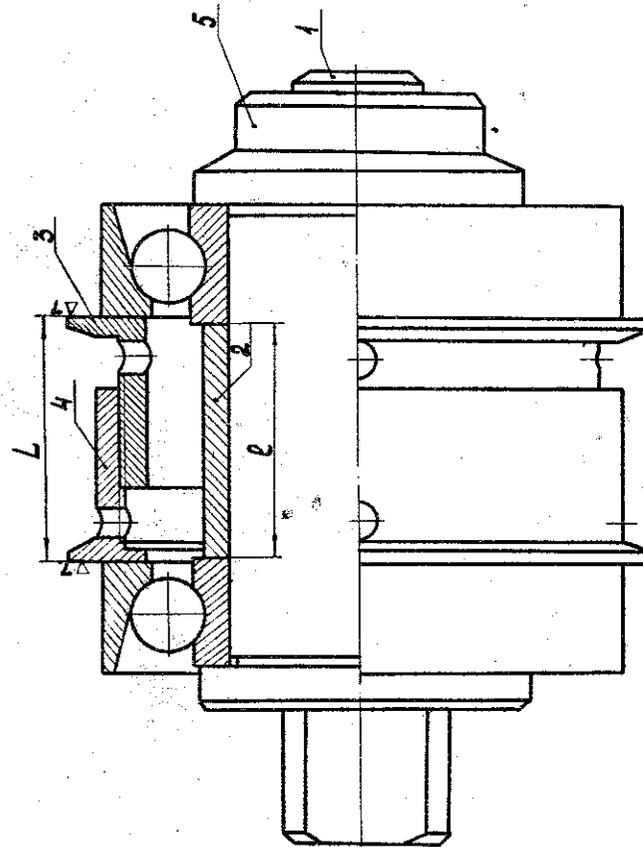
Приспособление для определения установочных размеров распорных втулок под радиально-упорные подшипники
